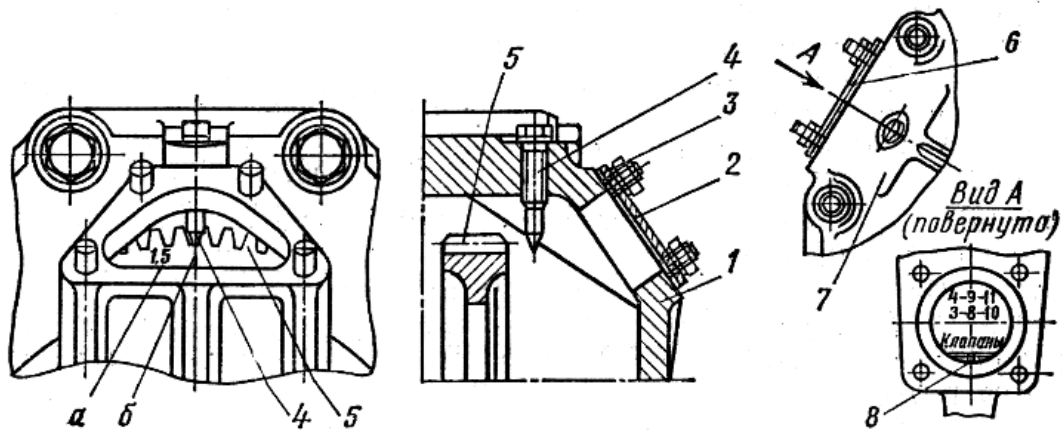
Вид на метки для регулировки клапанного механизма двигателя ЯМЗ-240Б:
